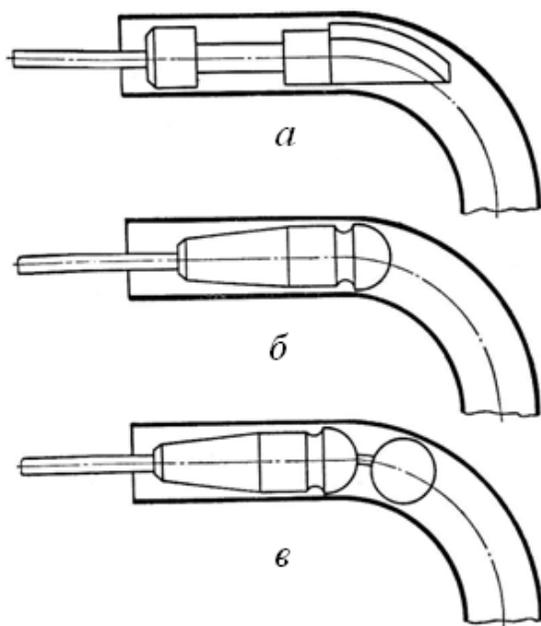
Схема гибки с применением калибровочных пробок:
